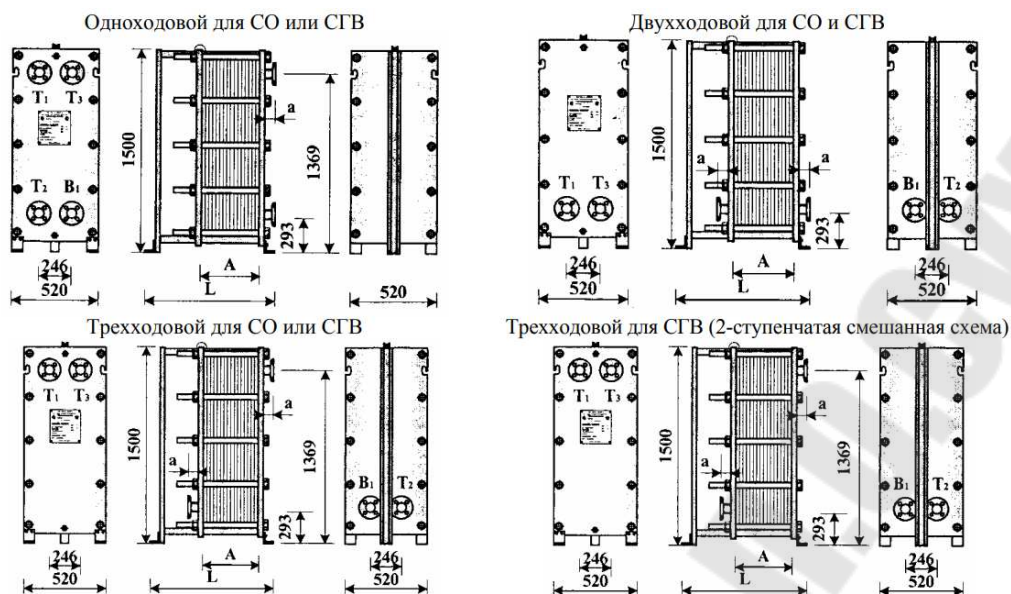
Общий вид, габаритные и присоединительные размеры пластинчатых теплообменников ТАР-0,4
